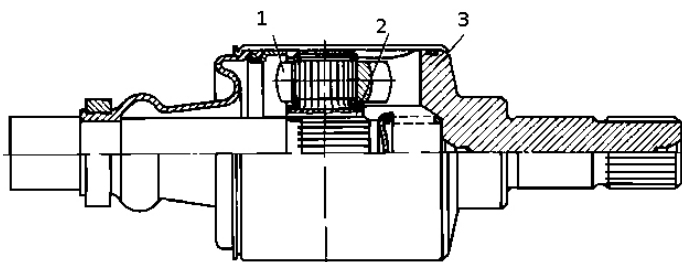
Трехшиповой универсальный карданный шарнир типа «Трипод»: 1 – ролики; 2 – ступица; 3 – корпус
